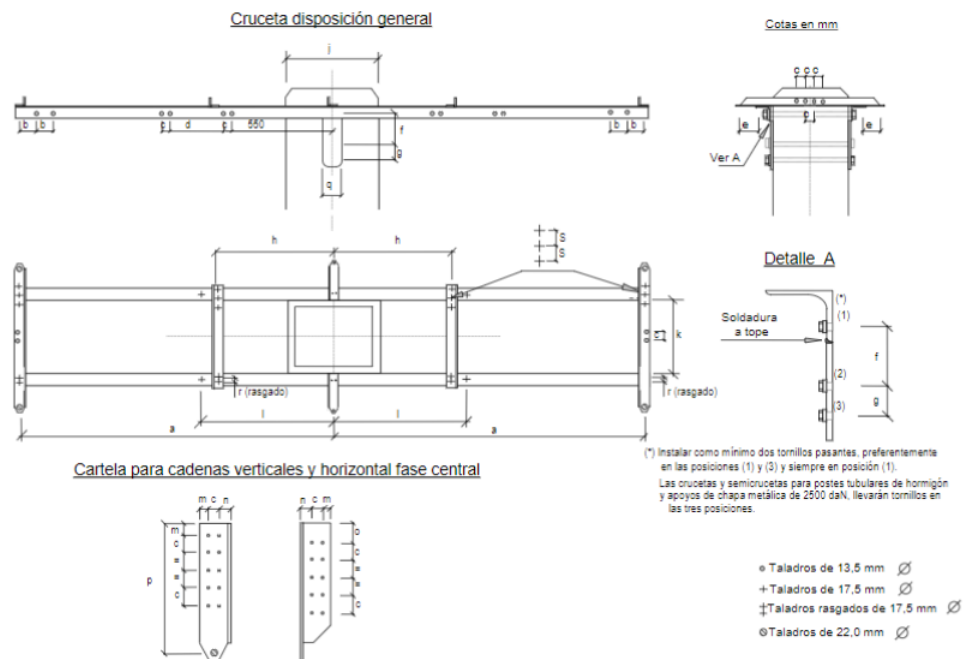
Crucetas para apoyos de hormigón y chapa metálica
